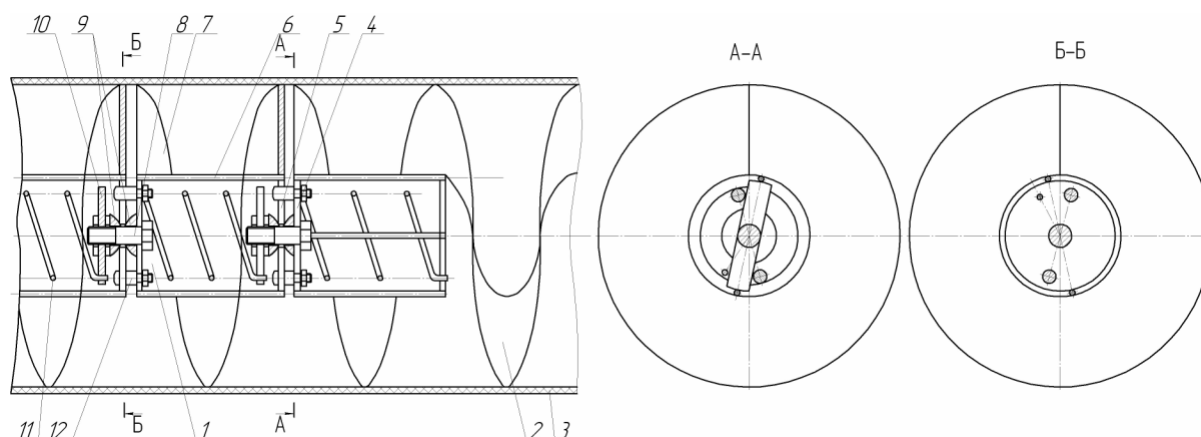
Пружний гнучкий гвинтовий робочий орган
